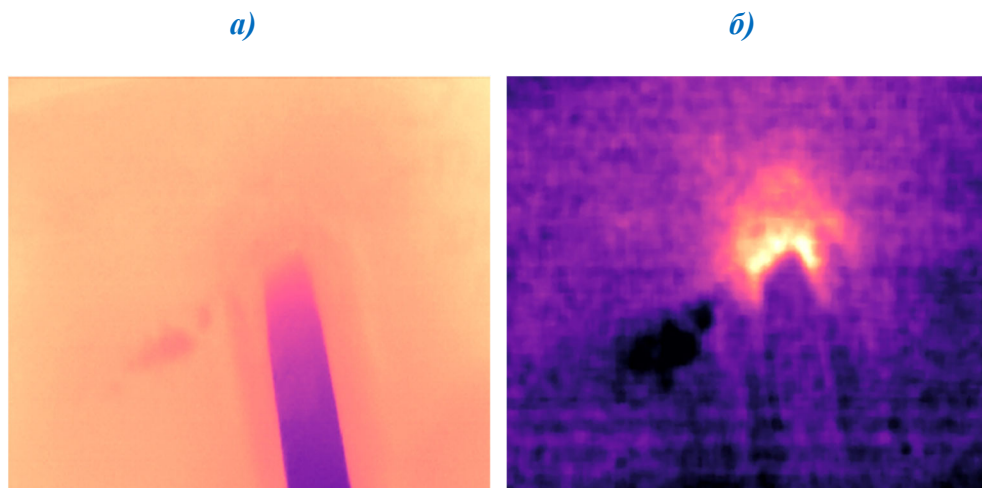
Образование усталостной трещины в сварном узле конструкции
